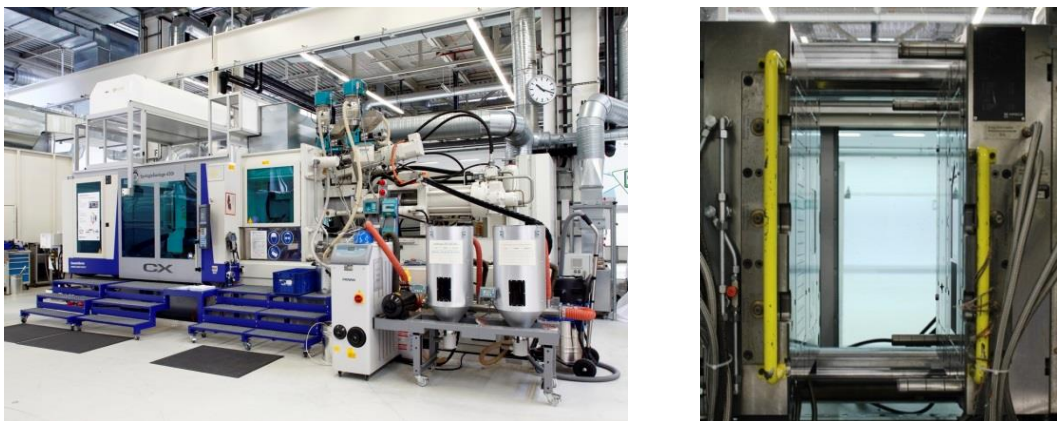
Spritzgussmaschine KM 650t (links) und eingebautes Normalienwerkzeug (rechts)
